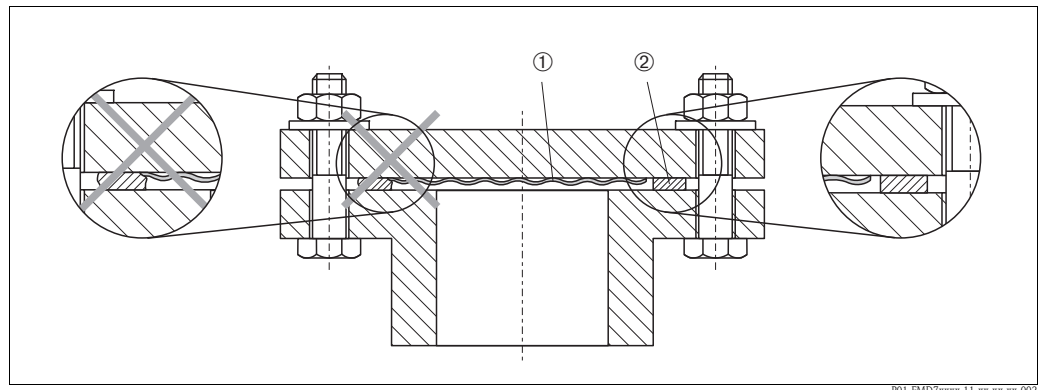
Montage der Versionen mit Flansch oder Druckmittler
